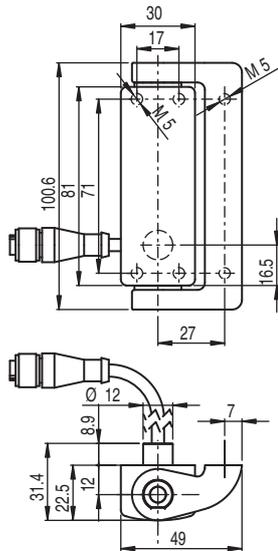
Dimensions du S400-Mx-CB02M12-W en mm
